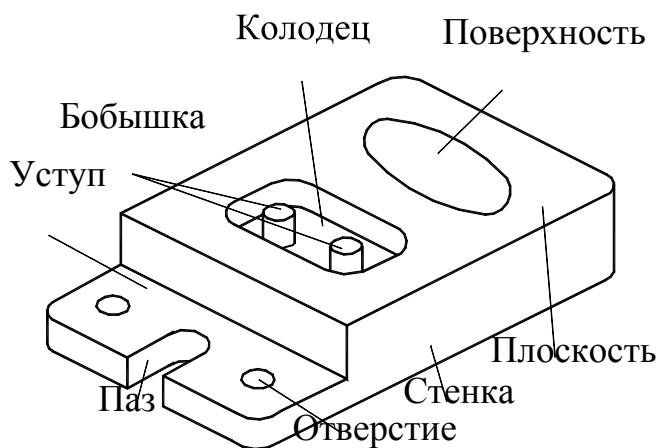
Обозначение элементов поверхностей при фрезеровании
